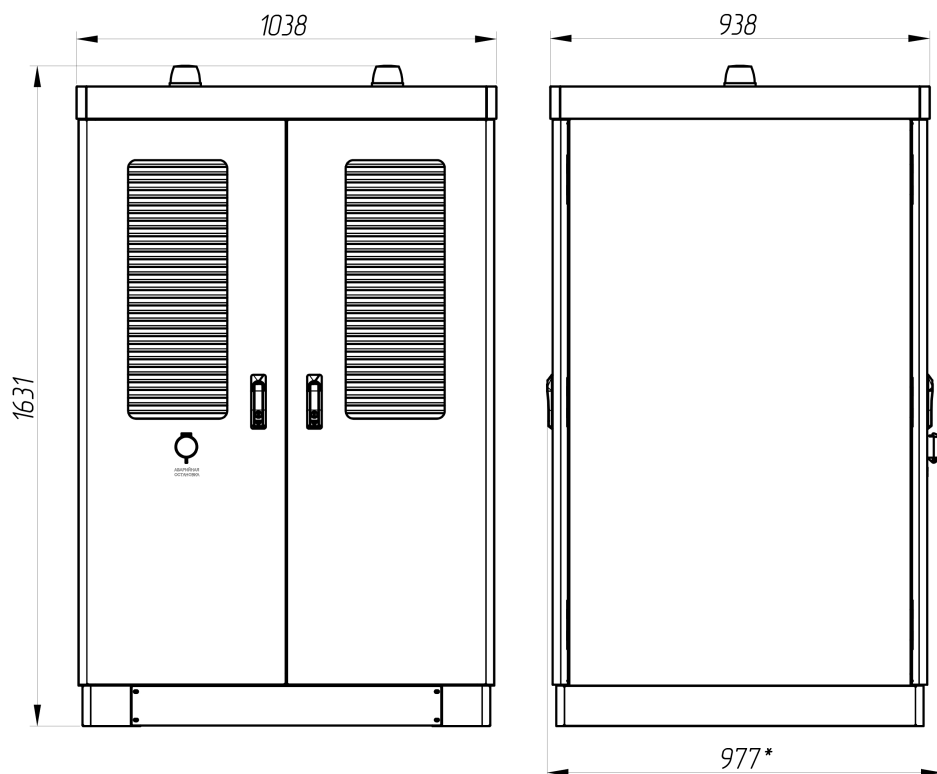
Габаритный чертеж модуля силового МС-300
